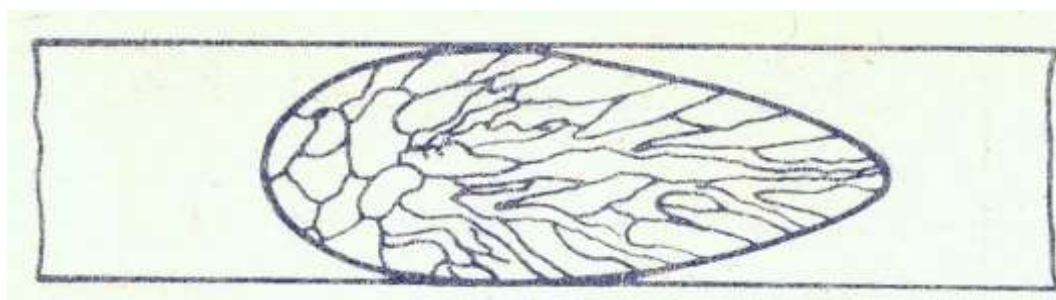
Кристаллическое строение сварочной ванны при мгновенном прекращении сварки
